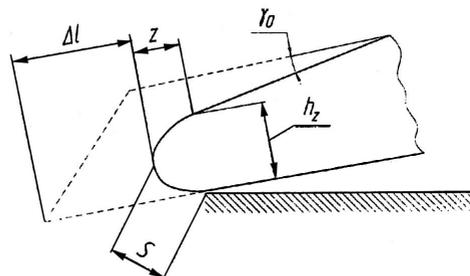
Самозатачивающаяся лапа конструкции ГОСНИТИ, с нижней наплавкой твердым сплавом
